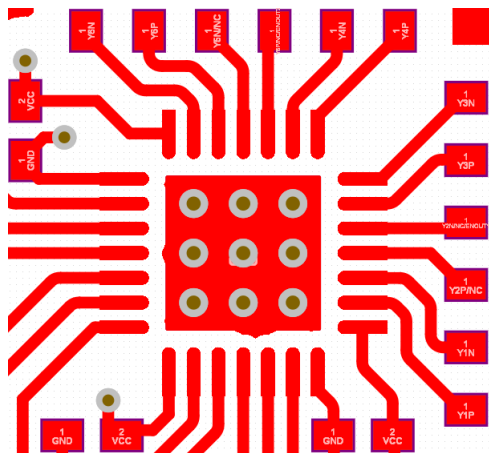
LMK1D2104L 的 PCB 布局示例，顶层
